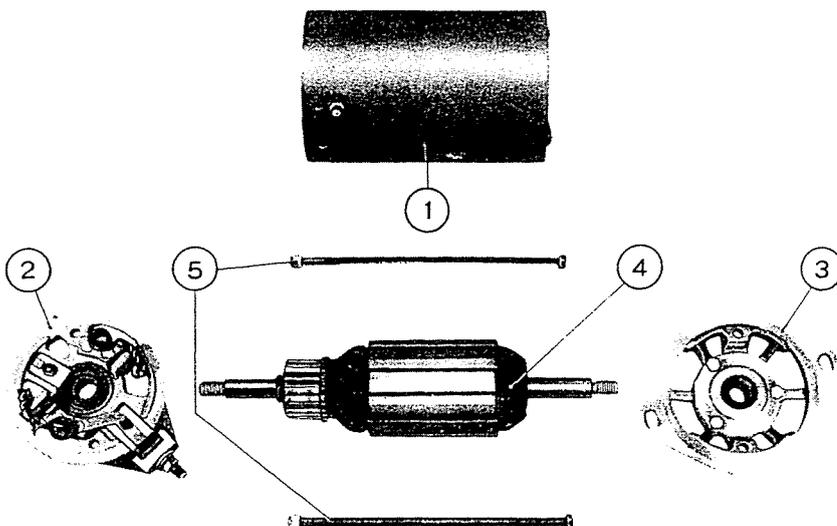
Bestandteile der Lichtmaschine DSV 90/12/16/3 S.
